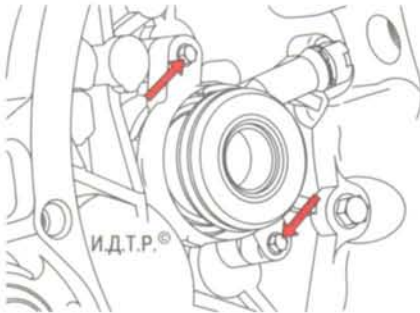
Расположение болтов крепления рабочего цилиндра гидропривода выключения сцепления
